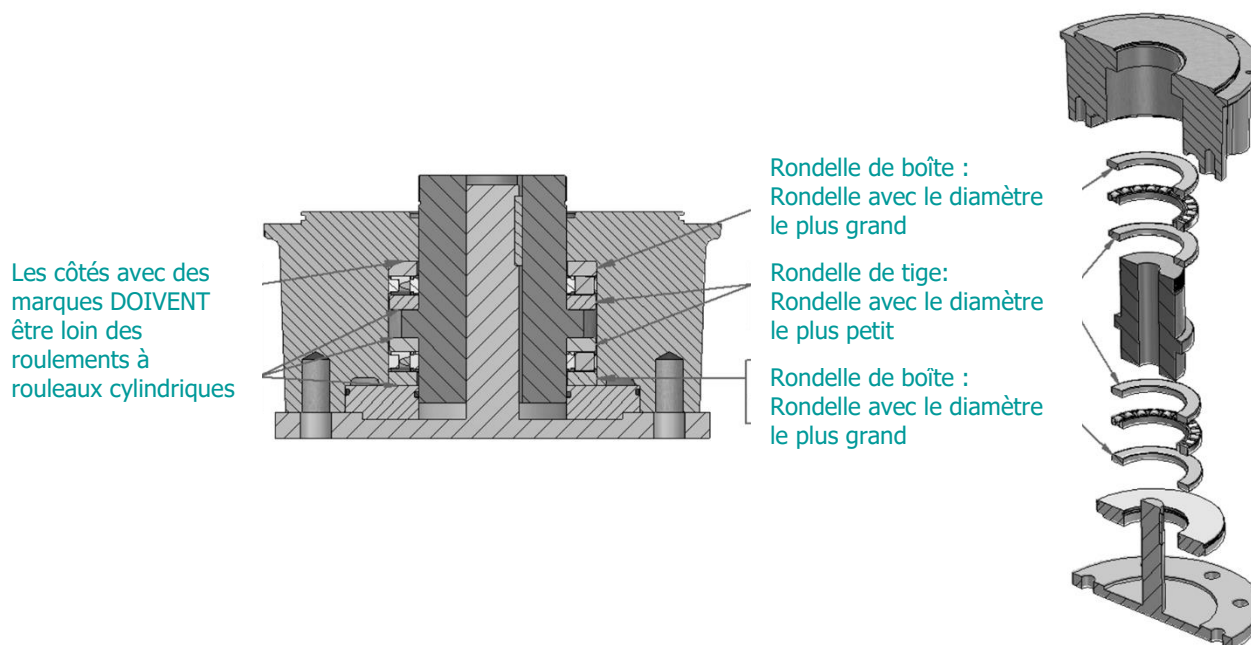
Assemblage de tige de vanne avec des roulements à rouleaux cylindriques
